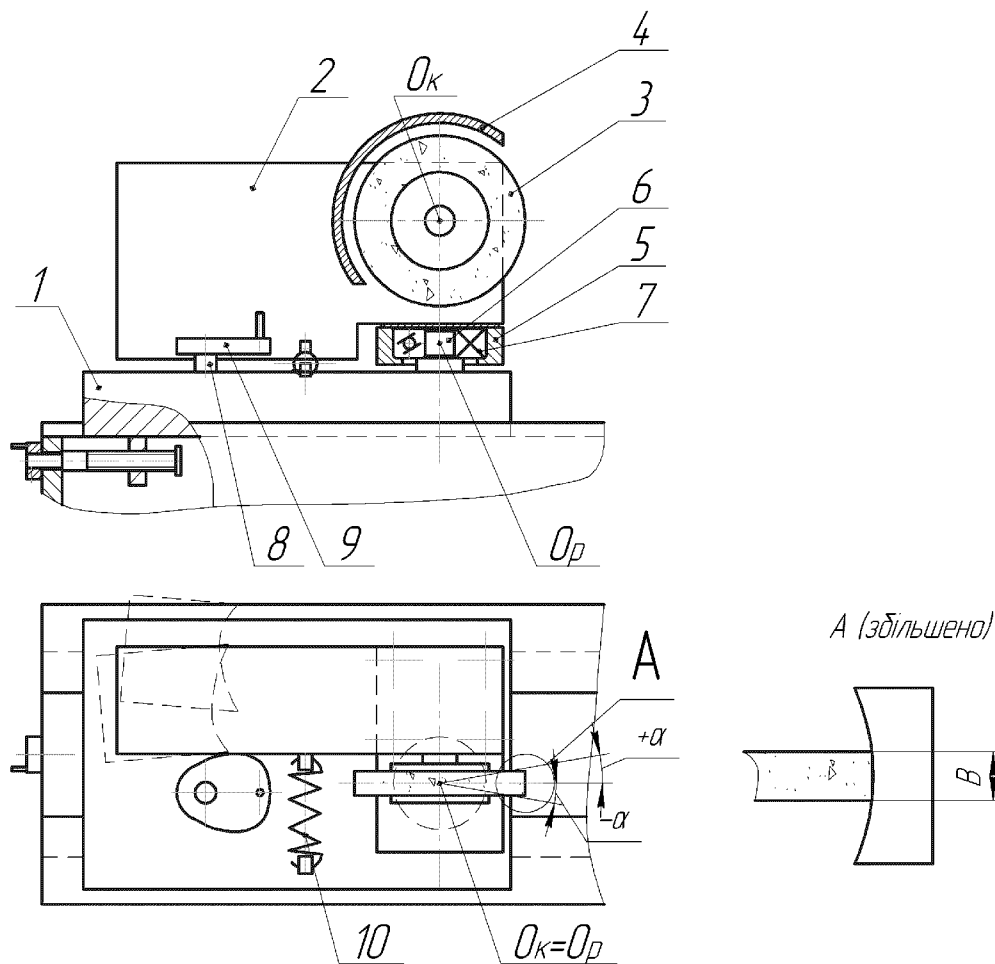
Принципова схема пристрою для шліфування сферичних поверхонь
